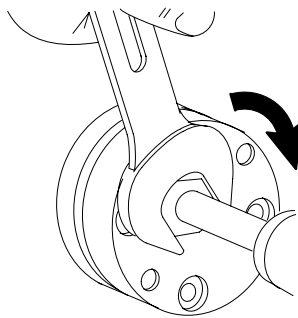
Stopfbuchsen-schraube der Pumpe festziehen (im Uhrzeigersinn)
